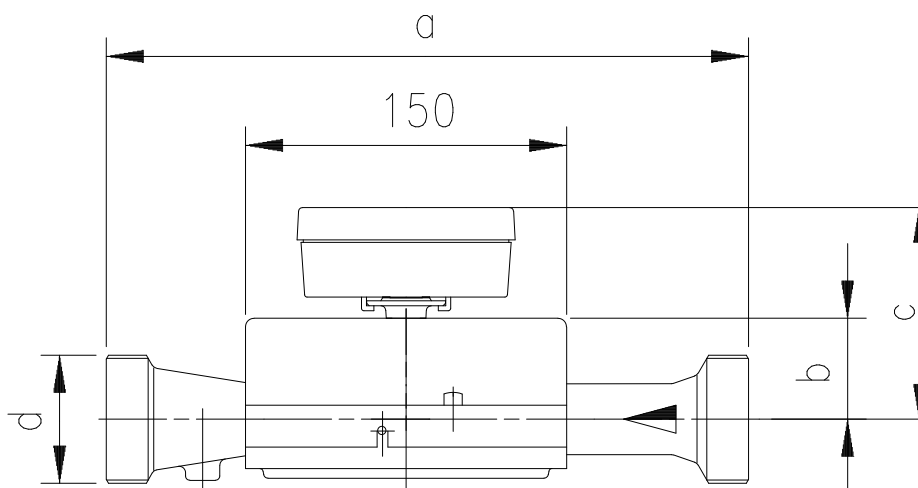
Габаритные и установочные размеры преобразователей расхода исполнений:
